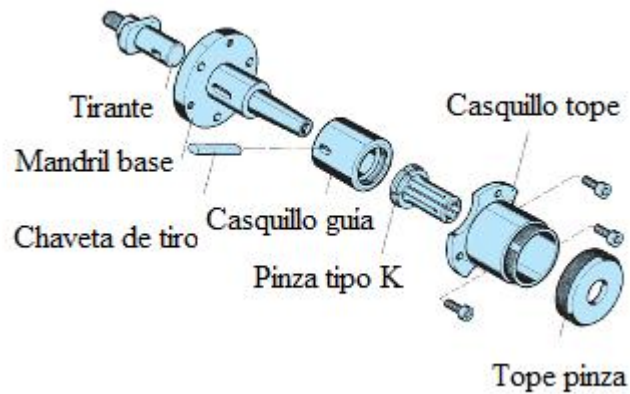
Mandril accionado automáticamente con brida portatopes [1]
